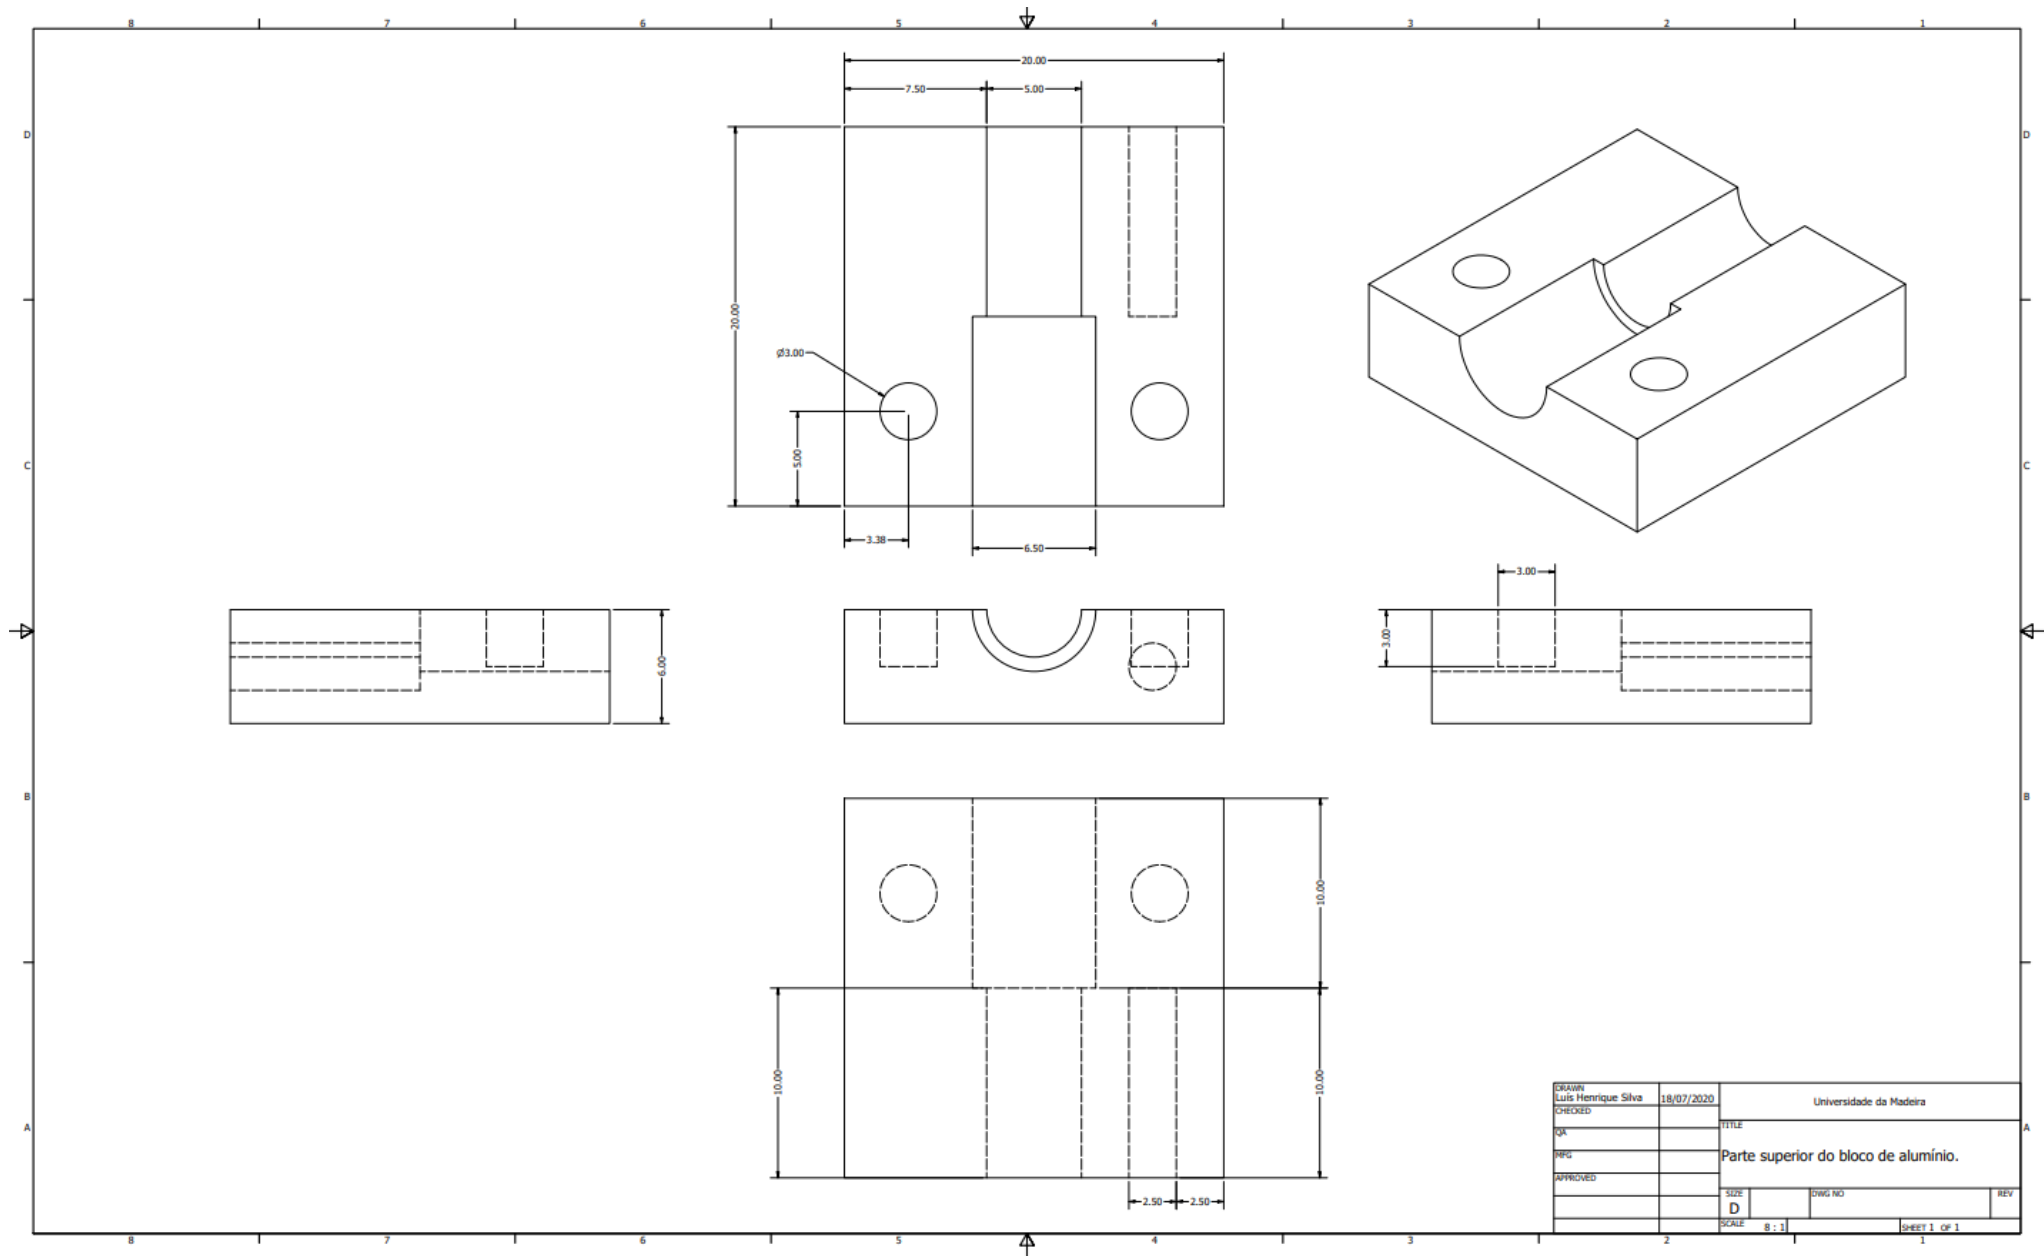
Desenho técnico da parte superior do bloco de alumínio.
